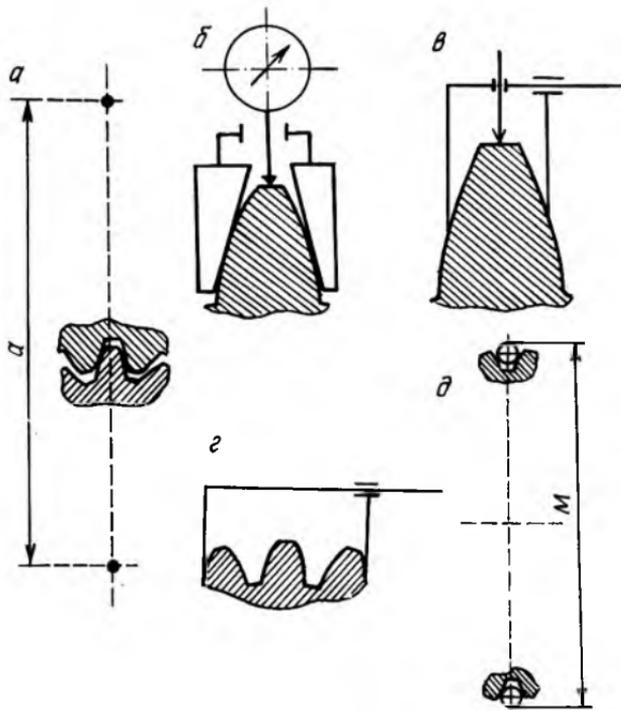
Схемы измерения показателей бокового зазора зубчатого колеса
